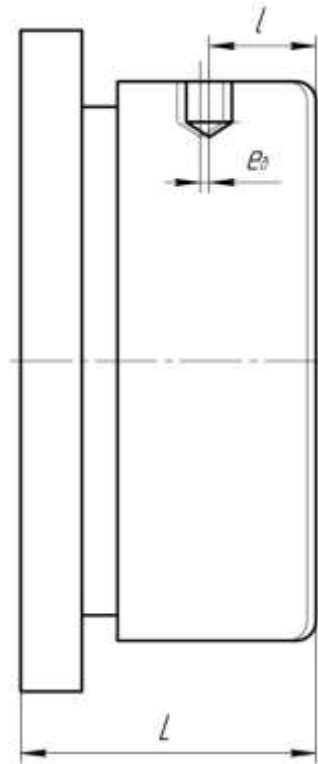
Схема для визначення похибки базування деталі стакан підшипника п'яти
